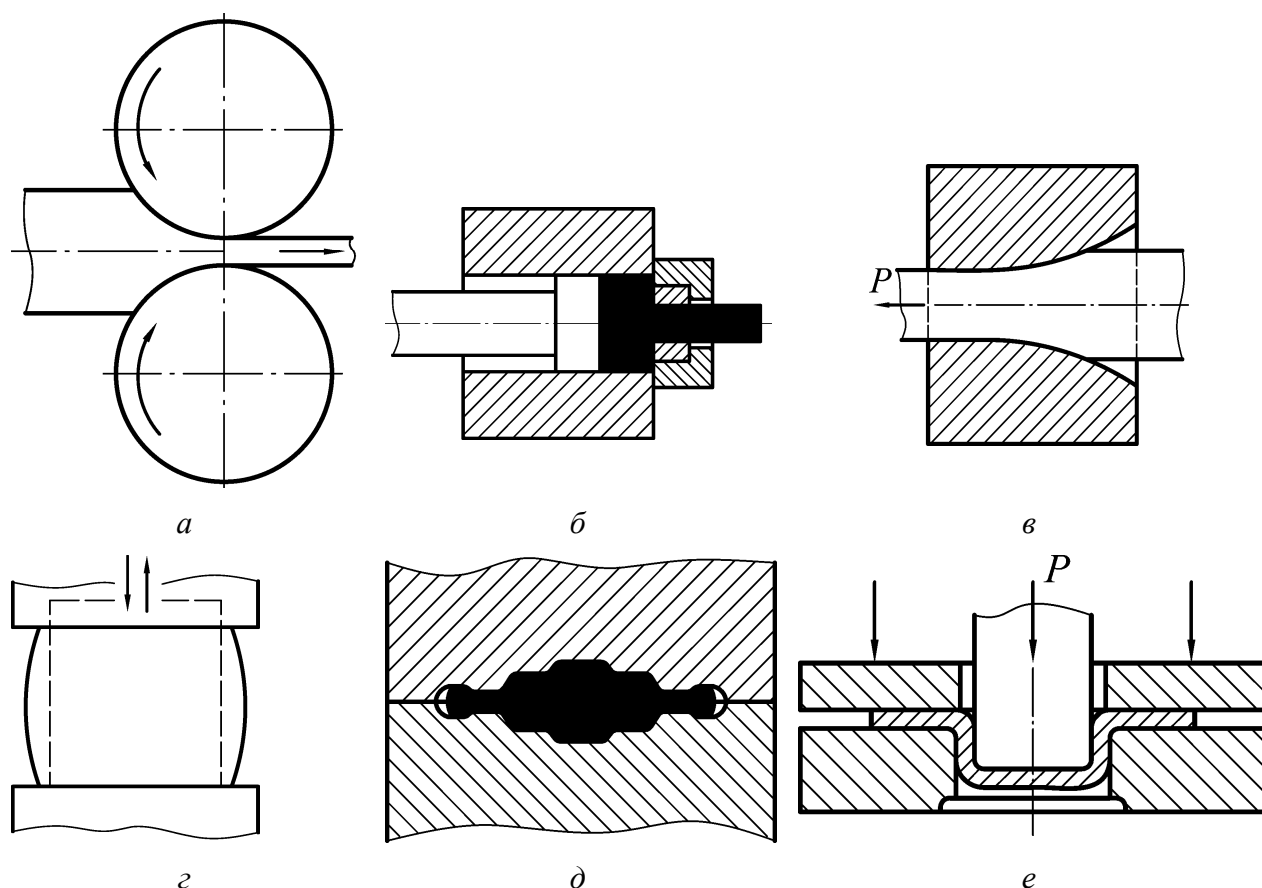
Схемы основных видов обработки металлов давлением: *а* – прокатка; *б* – прессовка; *в* – волочение; *г* – ковка; *д* – объемная штамповка; *е* – листовая штамповка
